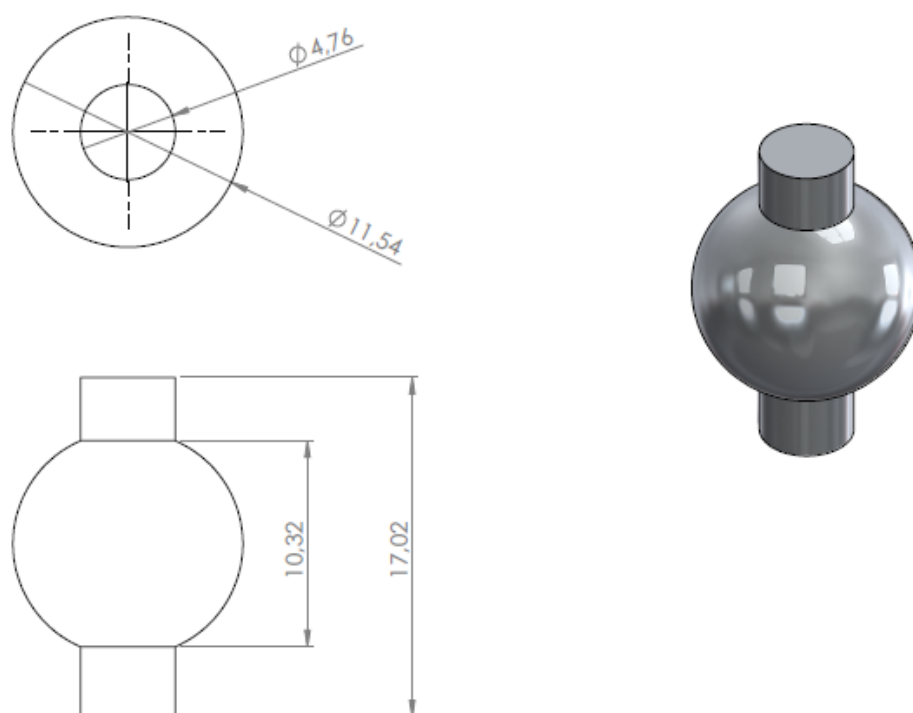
3D модель шарнира гексакоптера в SolidWorks
